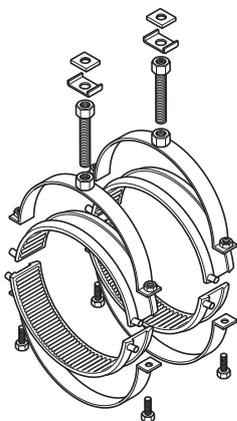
Кронштейн Geberit Pluvia с соединительной муфтой M16 и электросварной лентой
